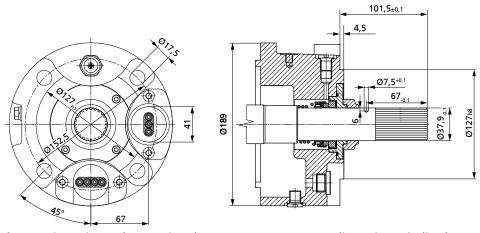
Dimensiones de conexión de UMA 200, UMA-S 200, dimensiones indicadas en [mm]
